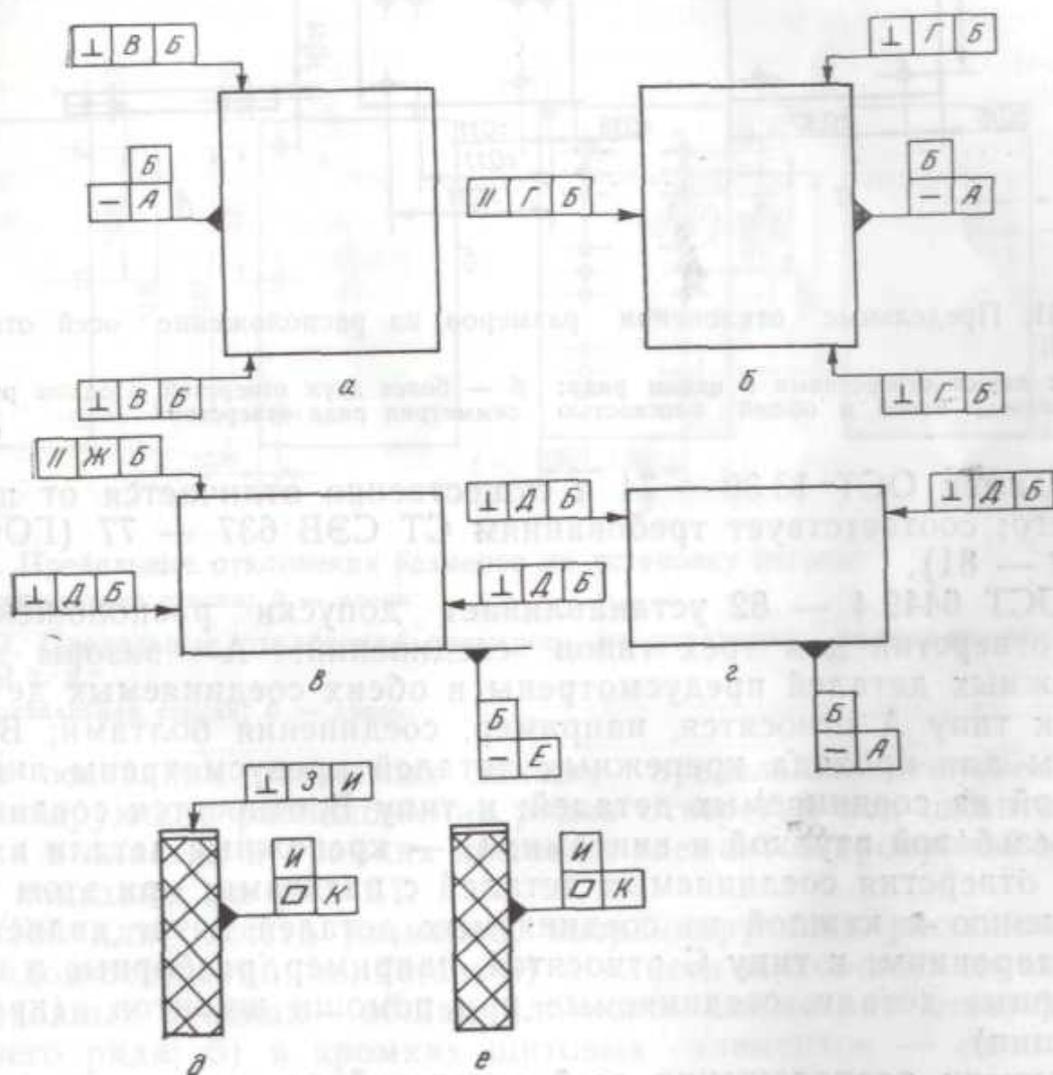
Обозначение формы, расположения поверхностей и баз:
